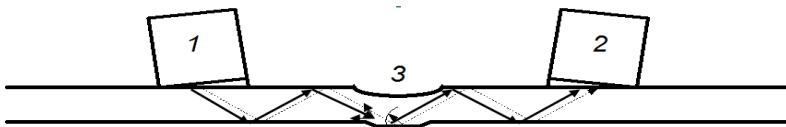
Геометрия лазерно-ультразвукового контроля в зоне сварного шва при наклонном вводе пучка: 1 — оптико-акустический излучатель; 2 — ПЭП (приемник); 3 — сварной шов
